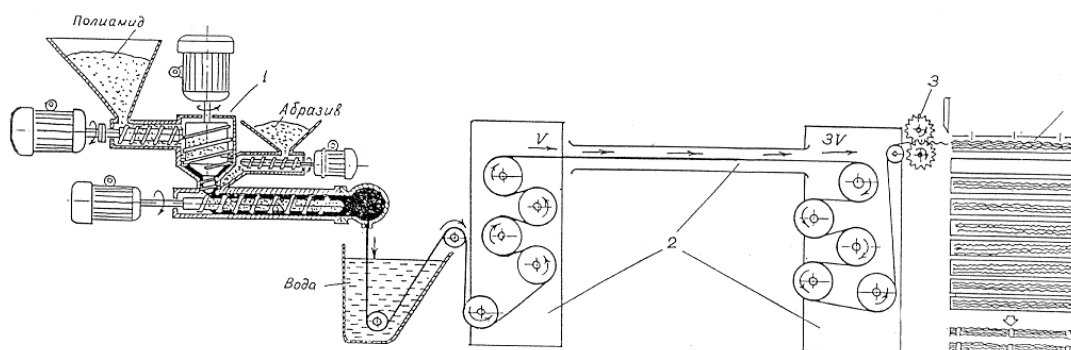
Схема виготовлення полімерно-абразивного волокна
